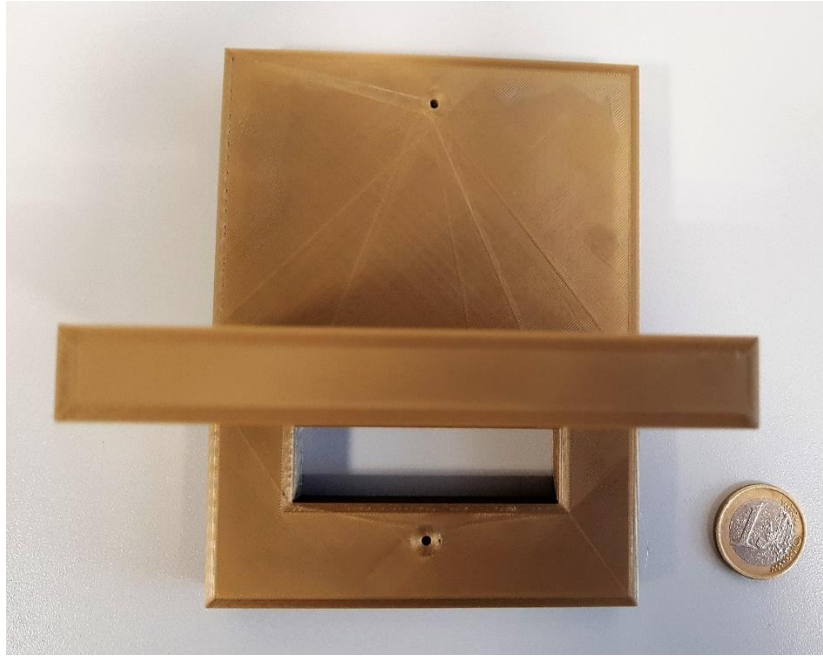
soporte fabricado mediante impresión 3D. Vista en alzado.
